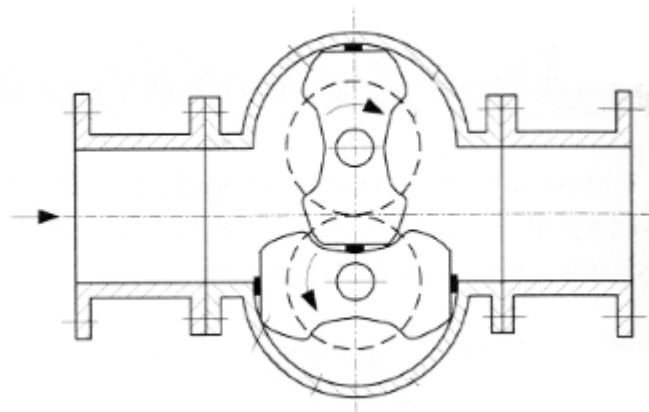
Oválný průtokoměr s hladkými okraji [3]
